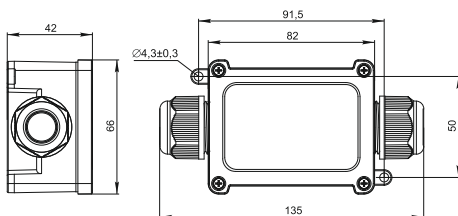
Габаритные размеры коробки WTP-410 / Figure 10- Overall dimensions of the WTP-410 box
